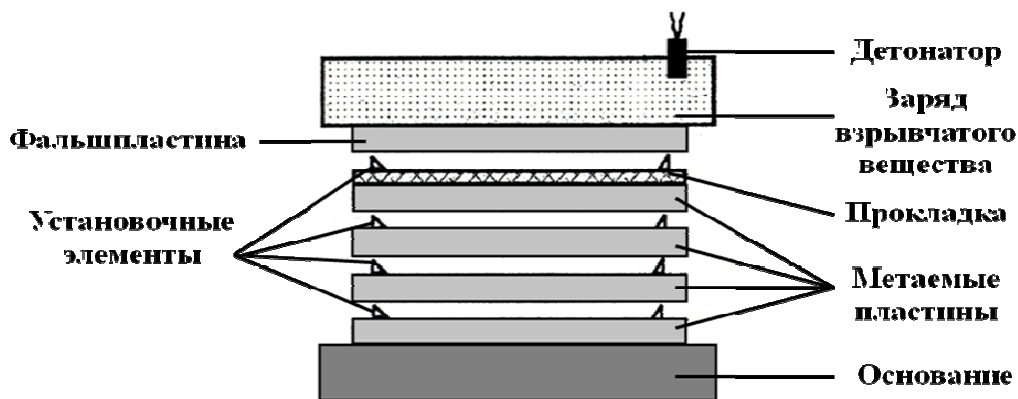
Схема сварки взрывом многослойных заготовок
